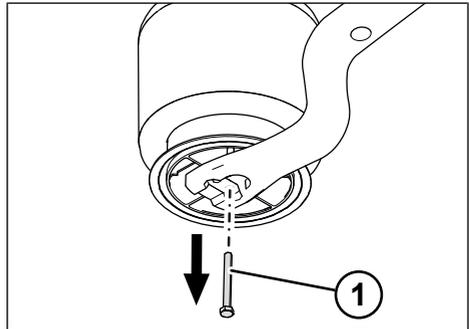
Verschraubung des Luftfederbalgs entfernen
